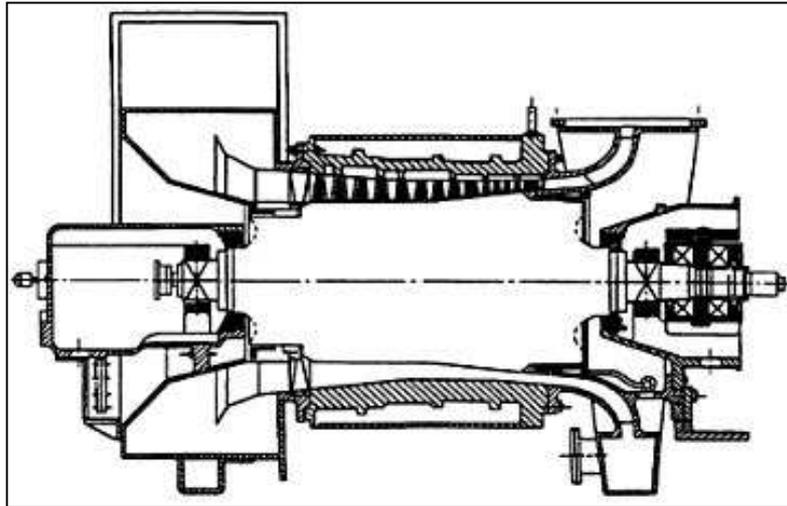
Compresor Axial de Múltiples Pasos
